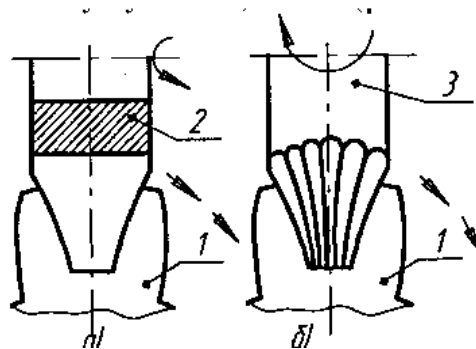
Схемы фрезерования цилиндрических колёс методом копирования: а – дисковой фрезой; б – концевой фрезой; 1 – заготовка; 2 – дисковая фреза; 3 – концевая фреза
